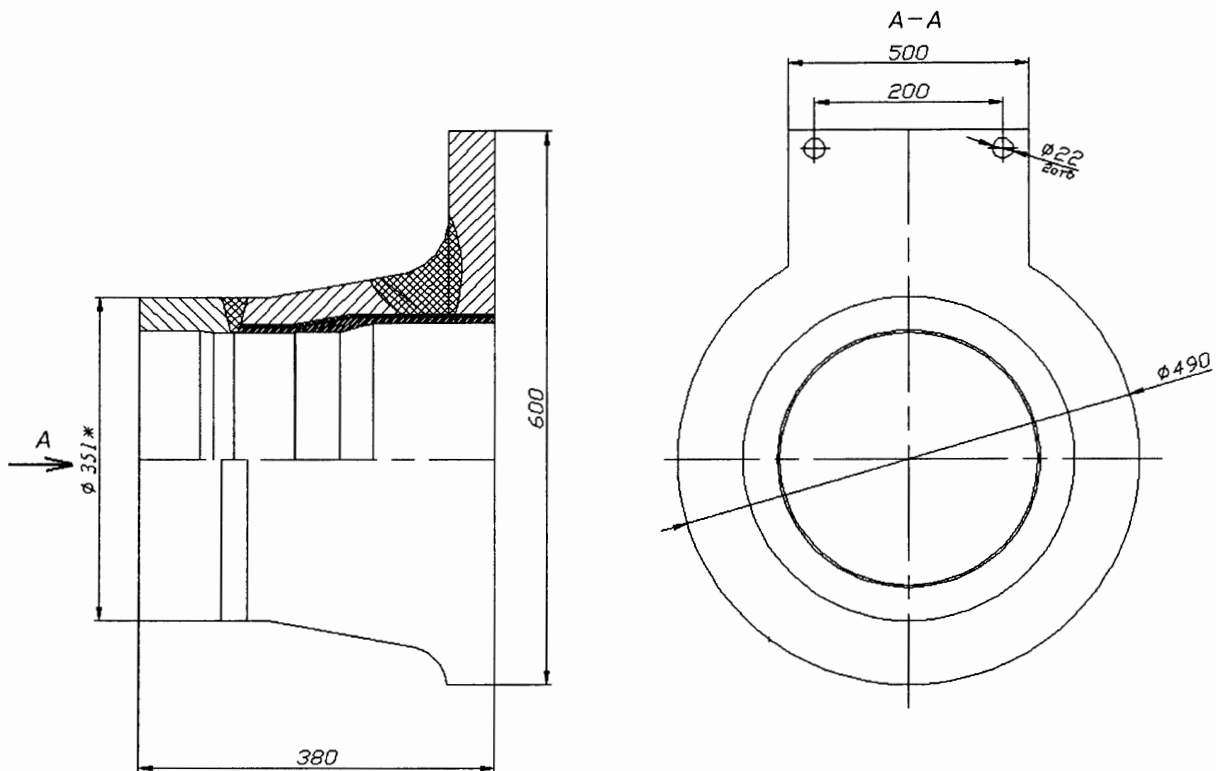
Образец-имитатор патрубка САОЗ
